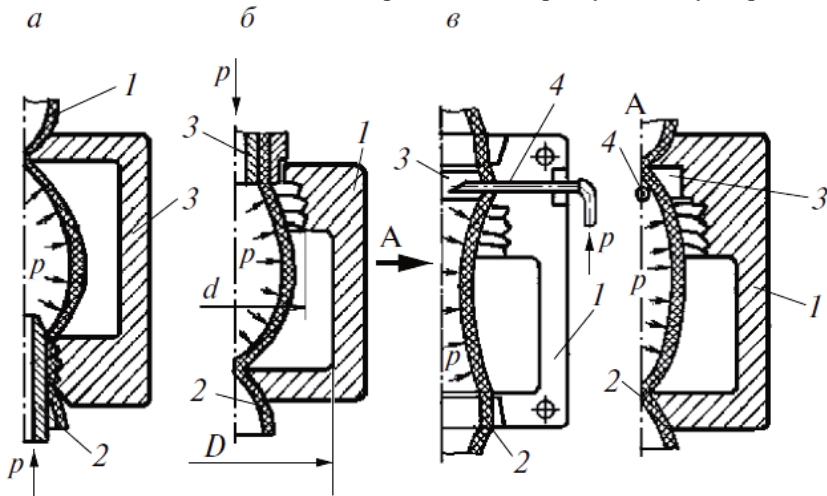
Способи роздуву трубчастої заготовки в формі
